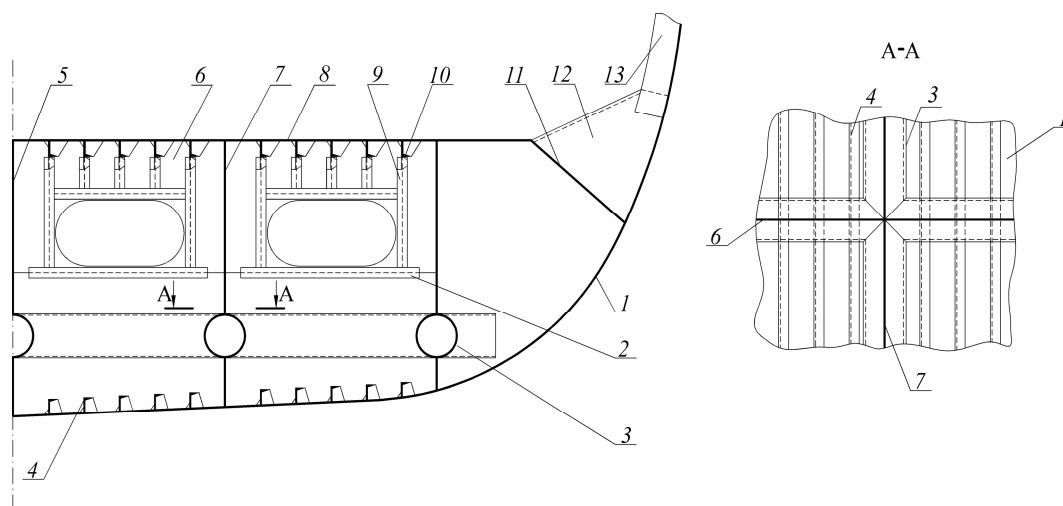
Схема днищевого перекрытия с трубчатыми элементами конструктивной защиты: а) – общий вид части днищевого перекрытия судна; б) – разрез А–А
